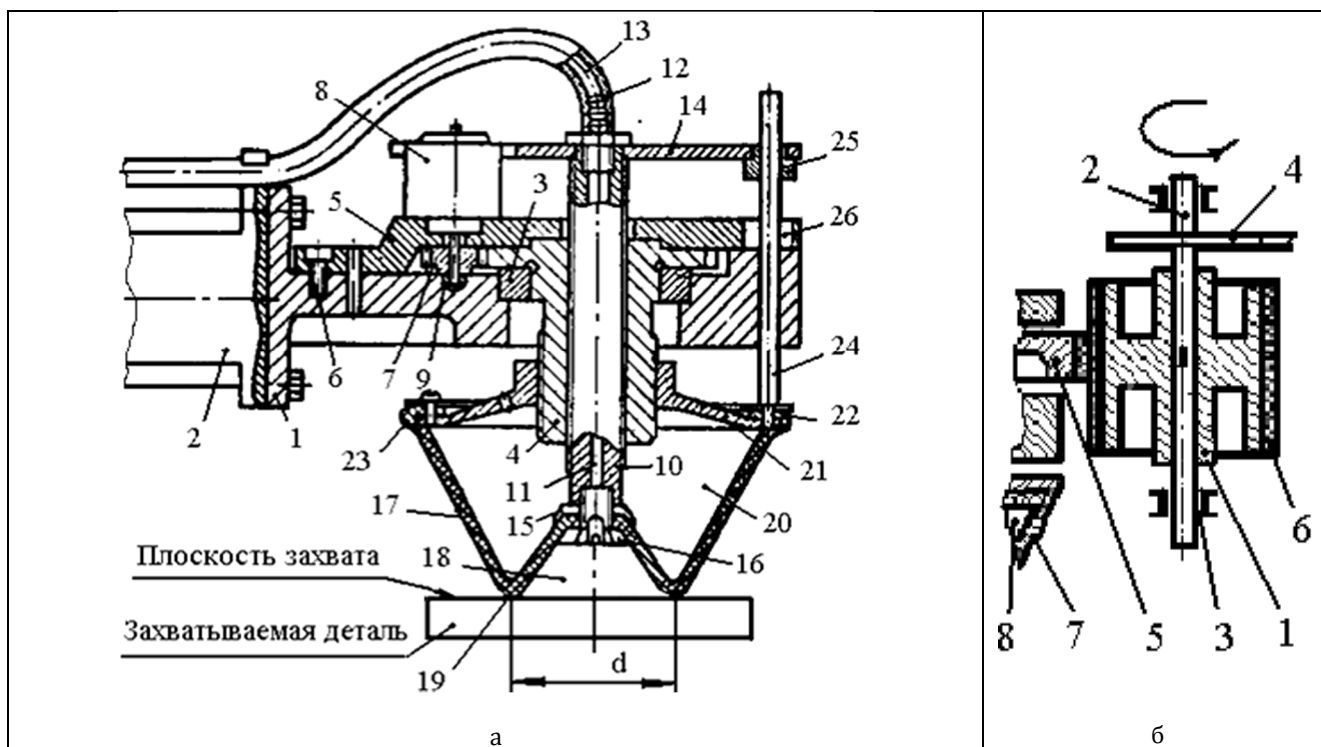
Захватное устройство вакуумного типа для промышленного робота с регулируемым диаметром вакуумной камеры: а – вертикальный разрез общего вида устройства; б – фрагмент исполнения с вынесенным приводом
